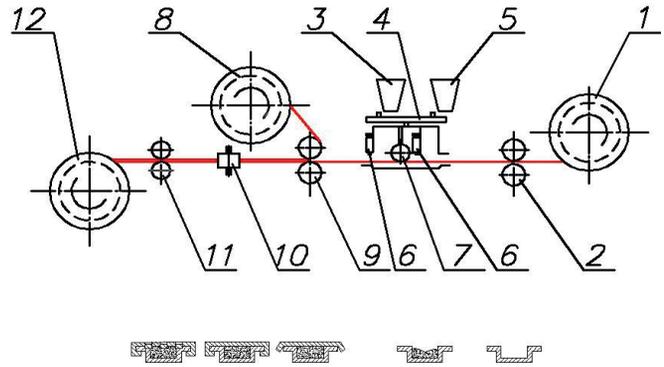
Схема протяжки порошковой ленты на станке: 1 – кассета металлической ленты для нижней части оболочки; 2 – формирующие ролики; 3, 5 – бункеры для компонентов; 4 – дозирующее устройство; 6 – ограничители высоты слоя шихты; 7 – уплотняющий ролик; 8 – кассета для металлической ленты верхней части оболочки; 9 – формирующие ролики; 10 – формирующие ролики замкового соединения; 11 – двухвалковая клет; 12 – бухта порошковой ленты
